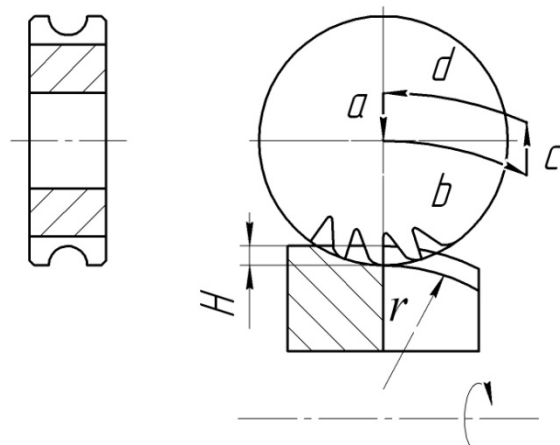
Схема закругления торцов зубьев дисковой фасонной фрезой
